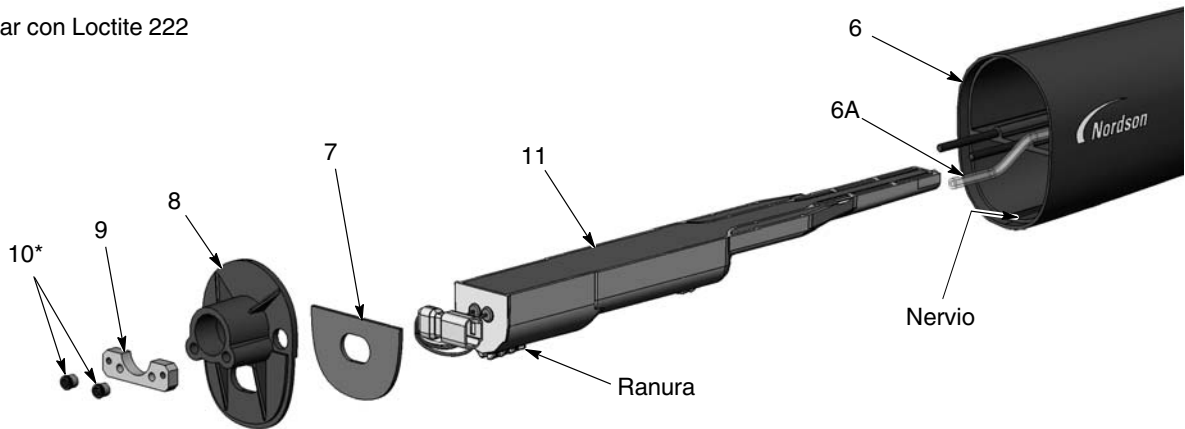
Desmontaje de la pistola de montaje en tubo 4 de 5
